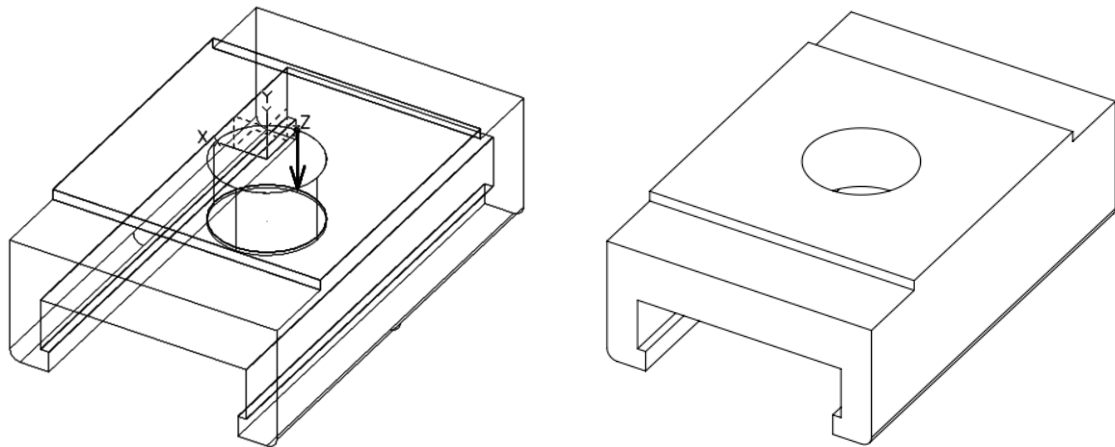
Vybrání materiálu tažením skici T drážky
